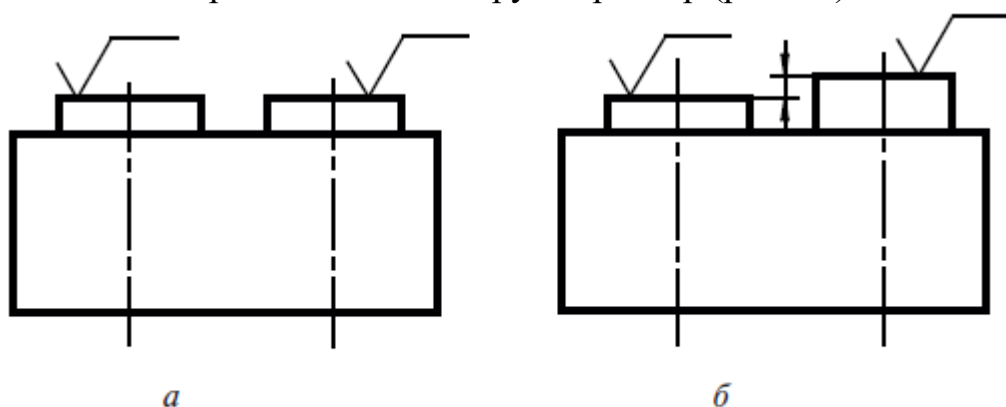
Конструкция корпусных деталей с бобышками:
